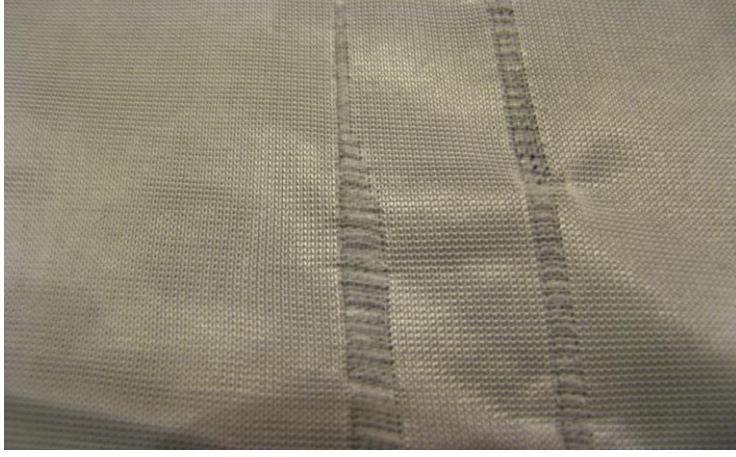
Düz örme makinesinde fırçaların ayarı; (a) mesafesi 1 mm [170]
